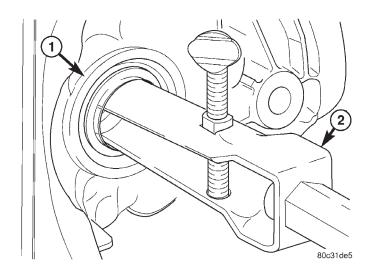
EXTRACTOR DE JUNTA DEL EJE
